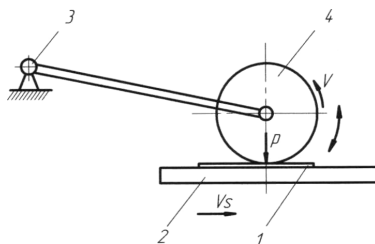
Принципова схема оброблення фрикційним зміцненням з маятниковим механізмом подачі інструмента-диска: 1 - деталь, що обробляється; 2 - магнітна плита; 3 - шарнір; 4 - інструмент-диск.
